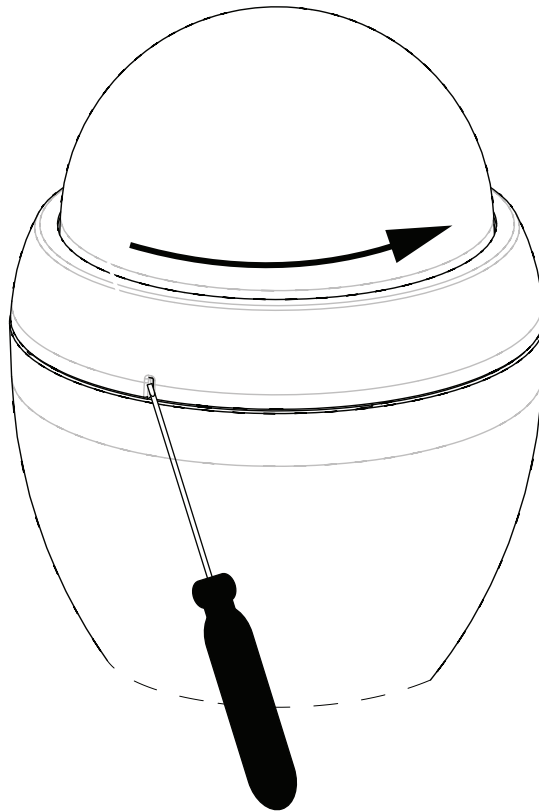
Сборка интерфейсной платы трубы и колпачка камеры
